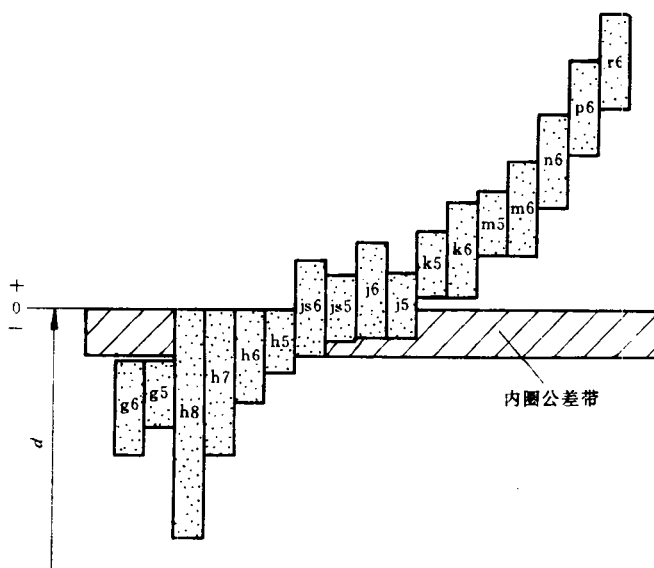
与滚动轴承配合的轴颈的常用公差带
